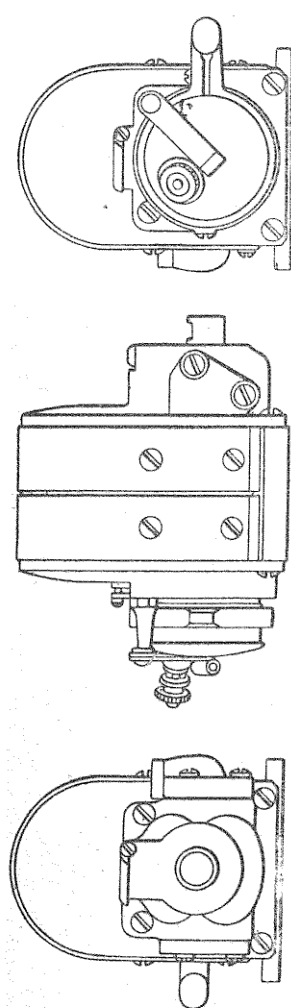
Magnéto Nihmelior type NA. 1 pour moteur monocylindrique. Vue de face du côté de la commande, vue de côté et vue de face du côté du rupteur.
